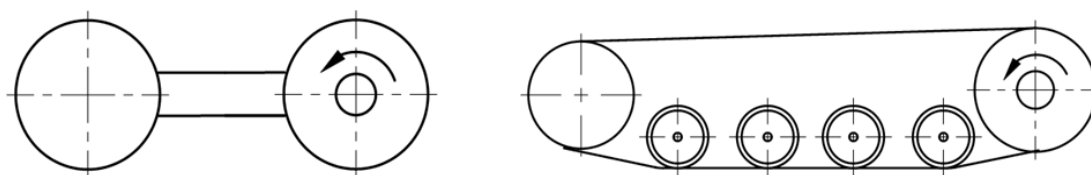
Схема сменного колесно-гусеничного движителя с поднятыми ведущим и направляющим колесом над опорной поверхностью
